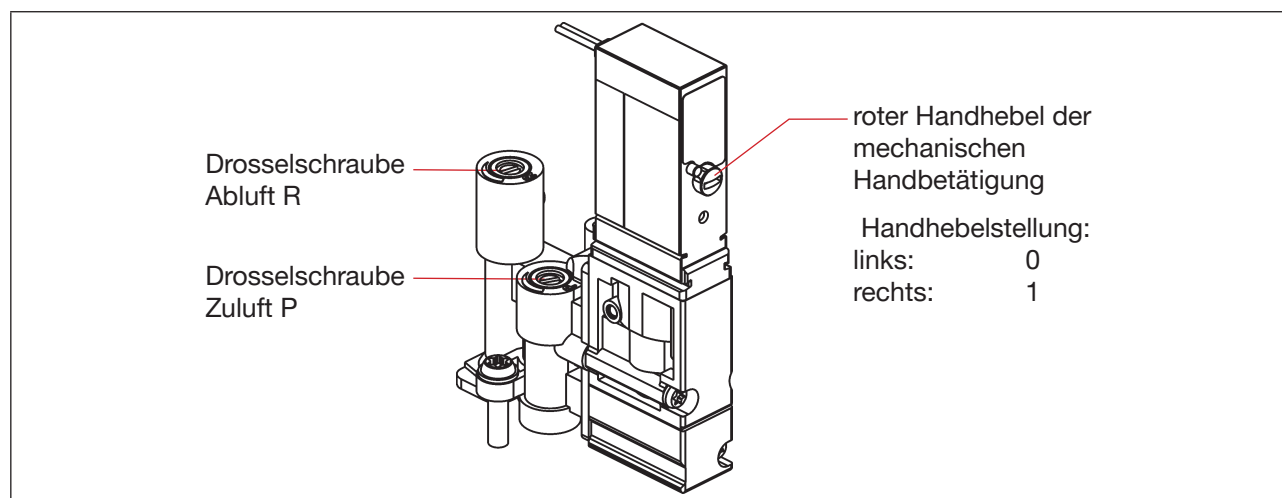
Drosselschrauben und mechanische Handbetätigung der Magnetventile
